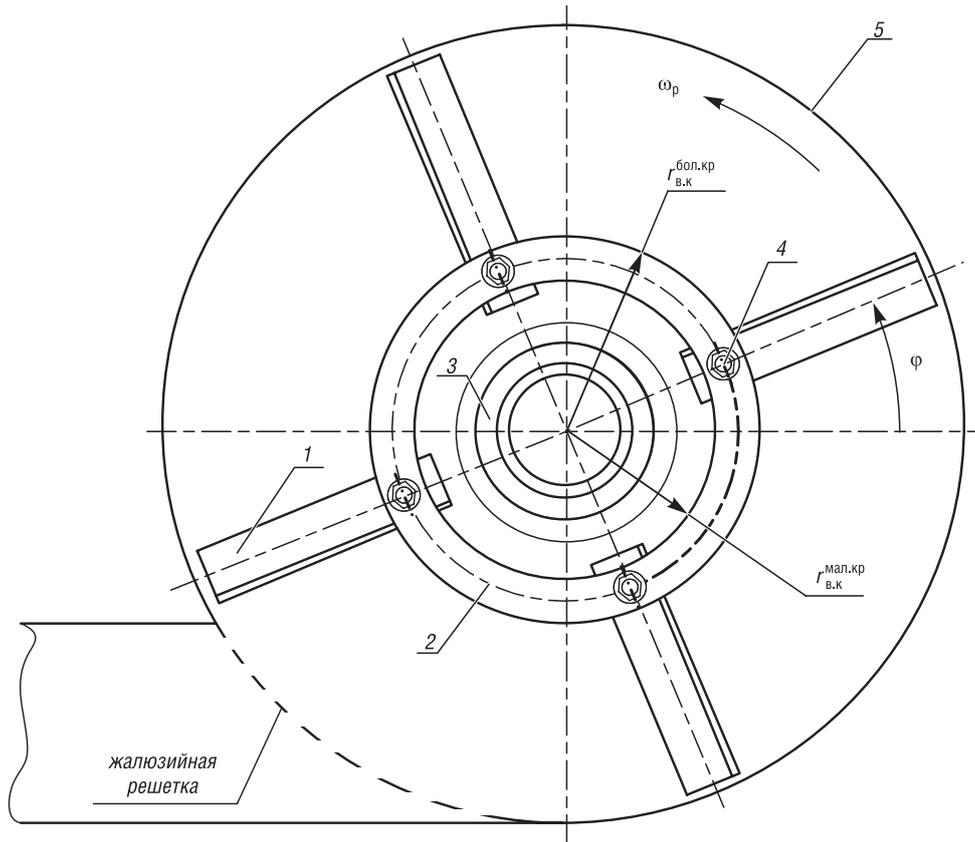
Схема модели движения роторного измельчителя: 1 – блок ножей механической системы; 2 – верхнее кольцо роторного измельчителя; 3 – нижнее кольцо роторного измельчителя; 4 – соединительный стержень (шпилька); 5 – корпус камеры сушилки-диспергатора
